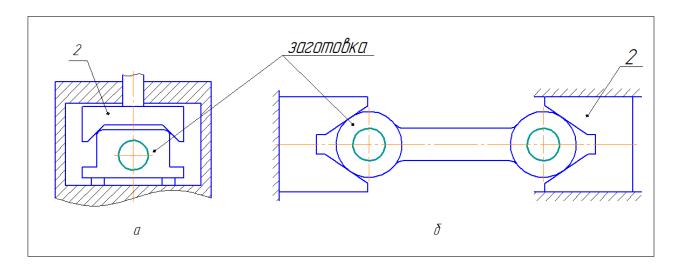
Зажимные устройства, выполняющие функцию центрирования: а – центрирование призматической заготовки; б - центрирование цилиндрической заготовки
